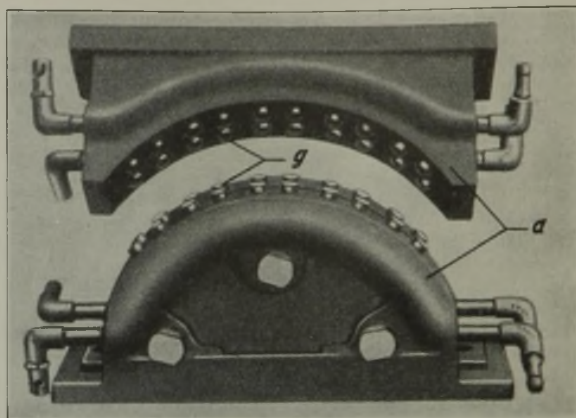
Sonderwerkzeug und Elektrode für die Projektionspunktschweißung.
